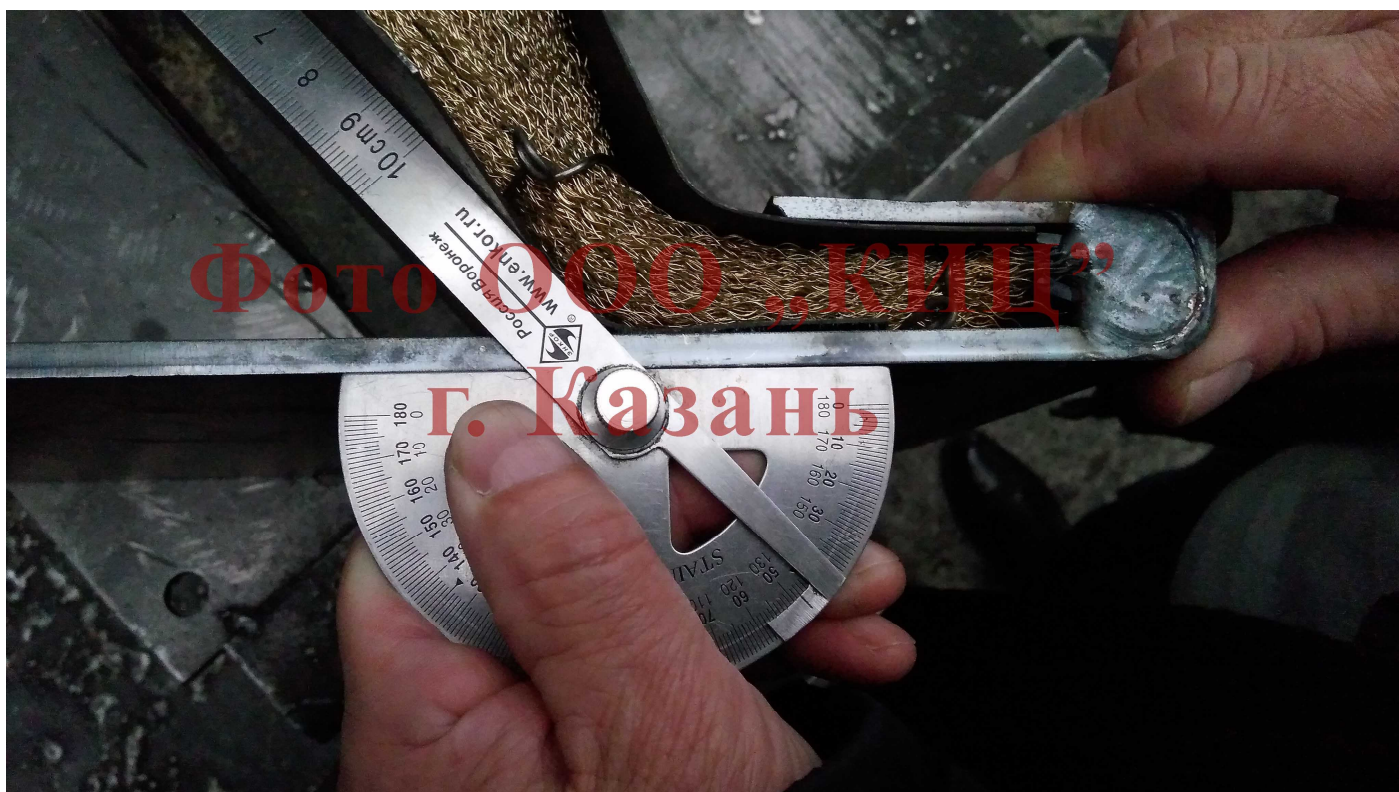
Угол сгиба задней пластины – 132 градуса (до испытаний)
